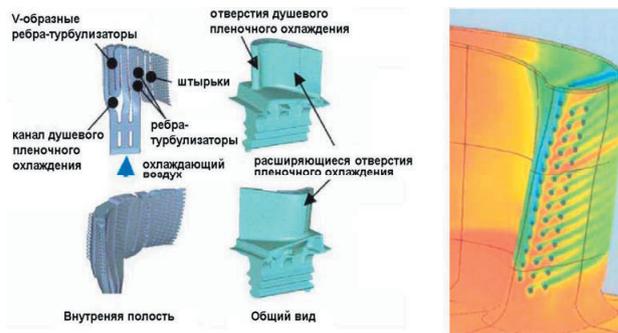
Рабочая лопатка первой ступени двигателя L20A фирмы «Кавасаки» [9]
